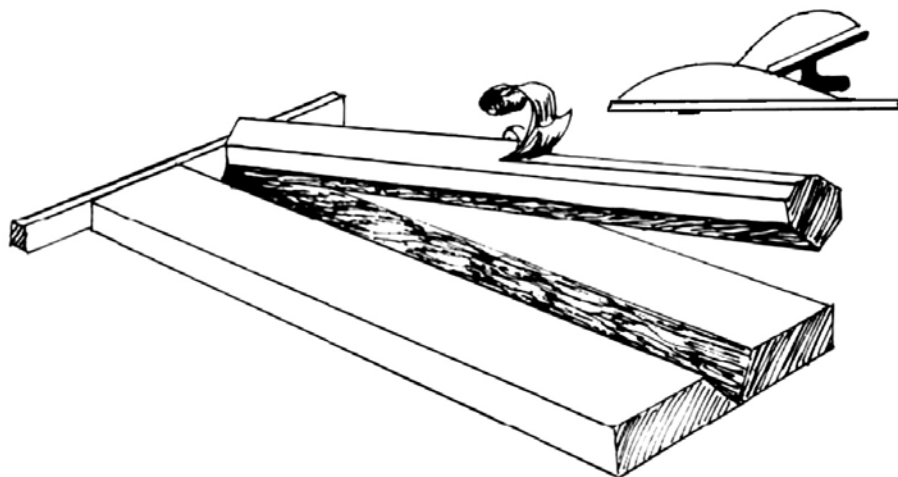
Приспособление для изготовления рангоутных деревеев.
